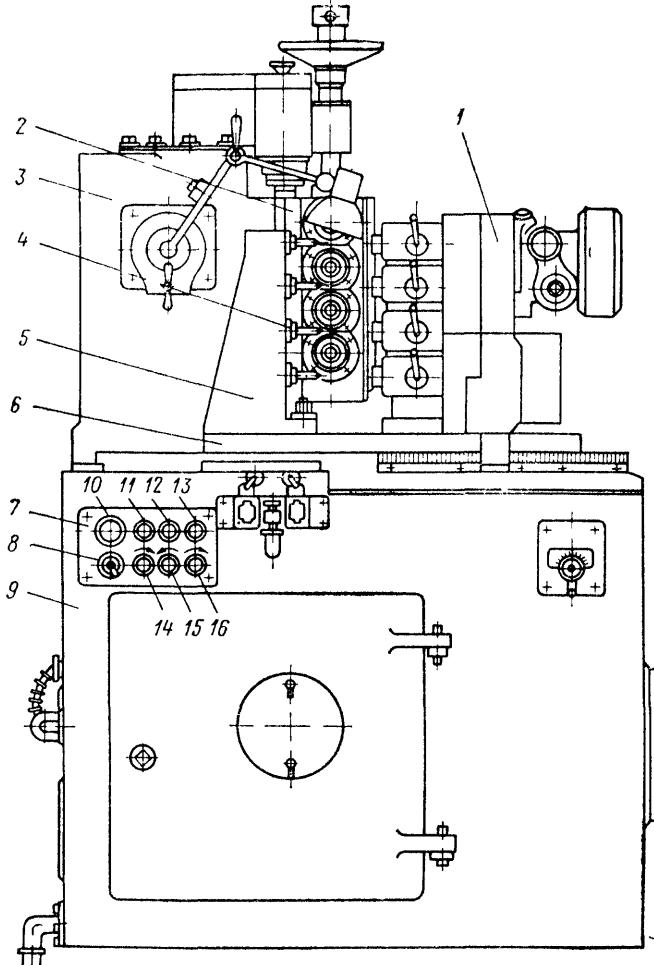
Специальный фрезерный полуавтомат модели СИ-040:
